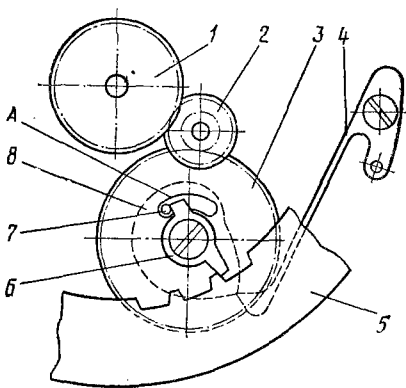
Кинематическая схема календарного устройства часов «Ракета» 2616:
